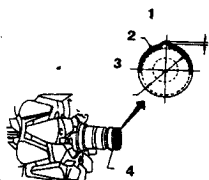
Положение установки заднего подшипника генератора (См. Раздел 8)
